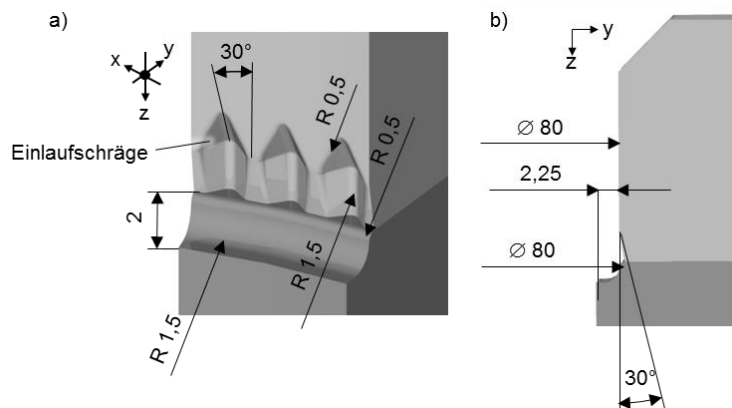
Maßnahmen zur Anpassung der Werkzeuggeometrie in a) 3D-Darstellung und b) in Seitenansicht
